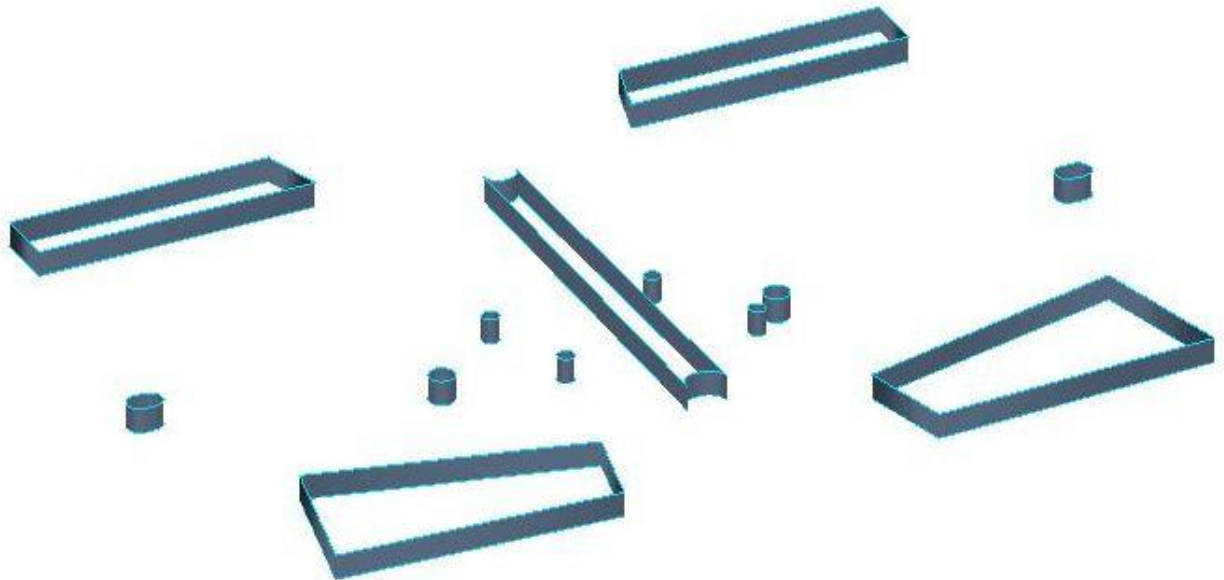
Рабочий инструмент для операций отрезки и пробивки отверстий
